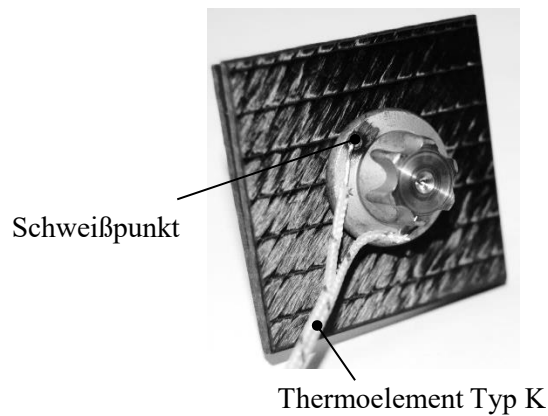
Prüfkörper mit an der Schraube angeschweißtem Thermoelement Typ K
